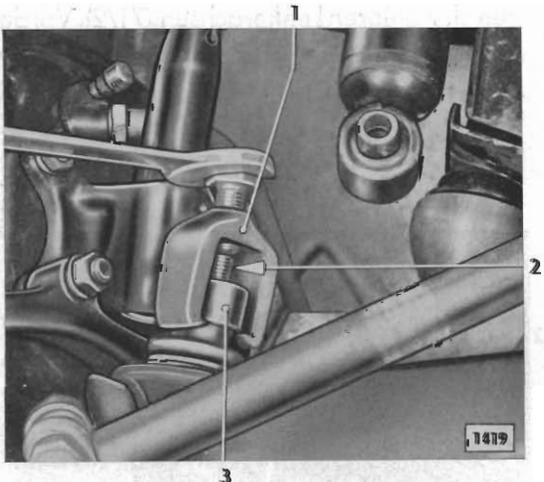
Achsschenkel vom Kugelbolzenschaft abziehen
